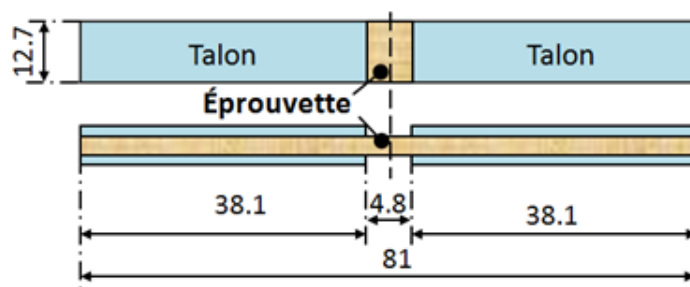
Dimensions des éprouvettes de compression, selon la norme ASTM D695 Boeing modifié
